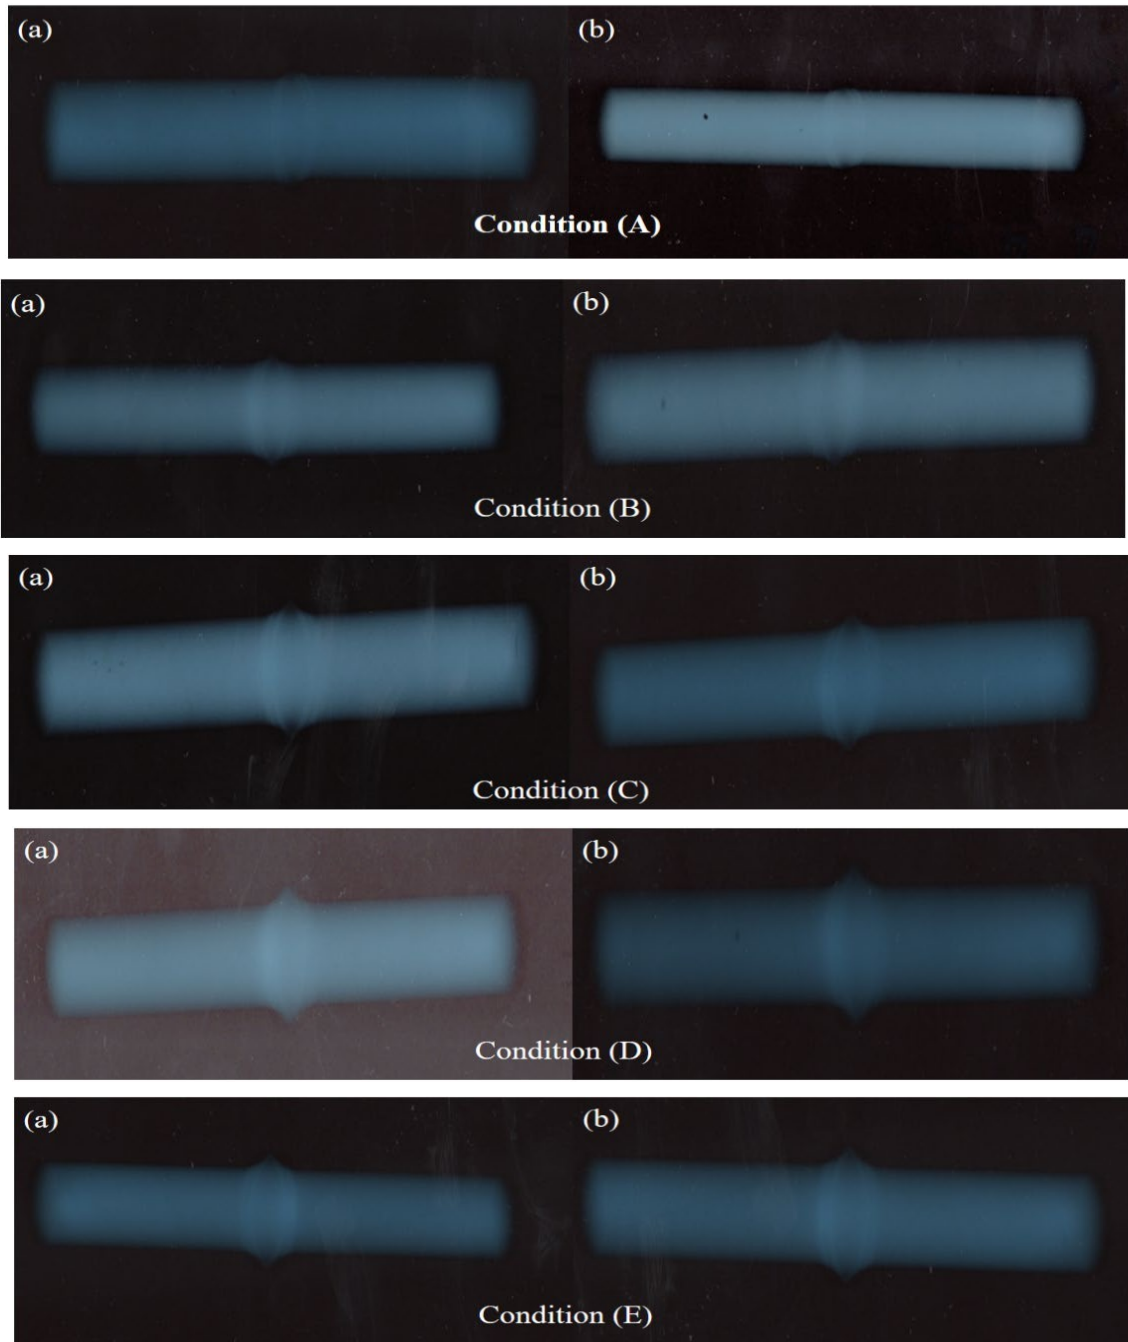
Contrôle par radiographie des joints A, B, C, soudés, conditions D et E)
